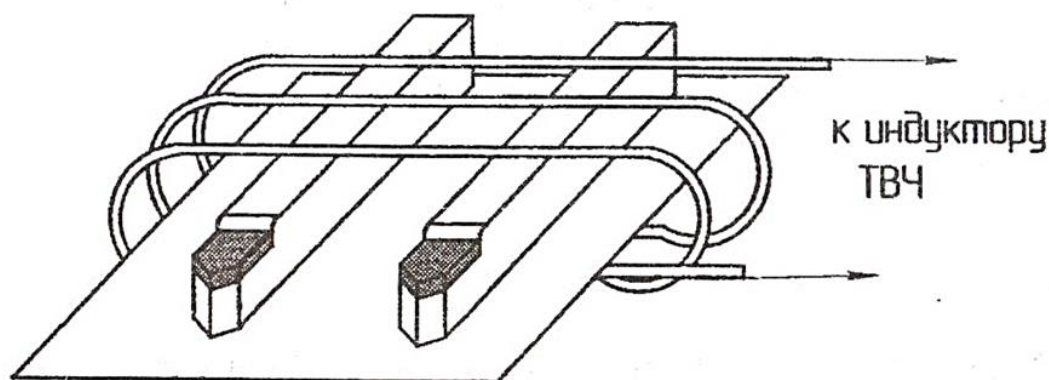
Схема нагрева резцов при пайке пластин
